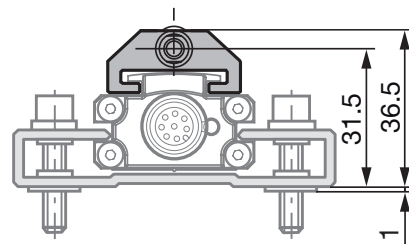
Dimensions et distances pour le capteur de position BTL5-T-2814-1S
